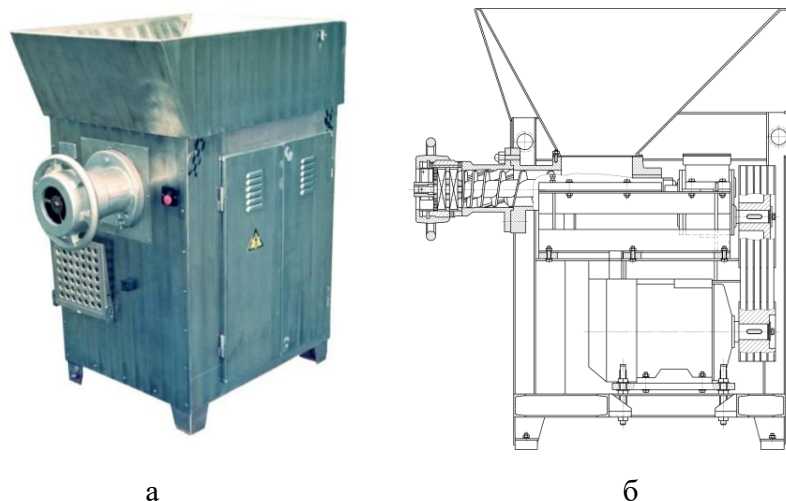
Вовчок-м'ясорубка марки К7-ФВП-160 [3]: а – вид загальний; б – конструктивна схема
